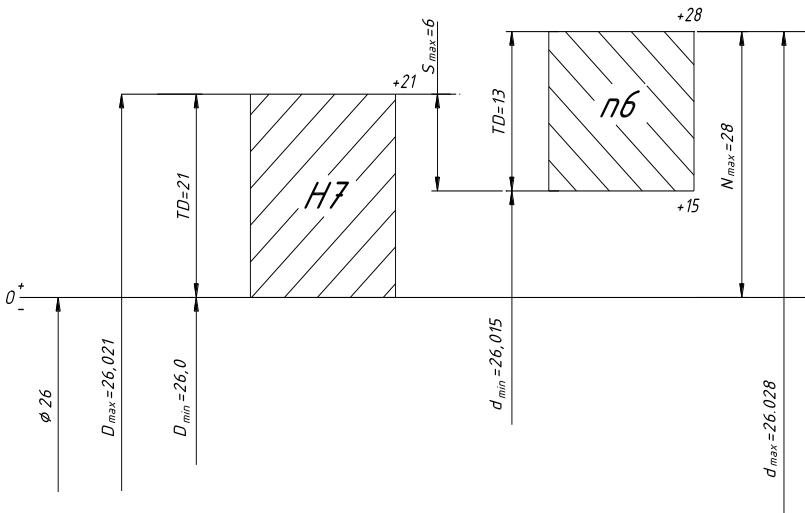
Схема розташування полів допусків з'єднання $\varnothing 26 \frac{H7}{n6}$
